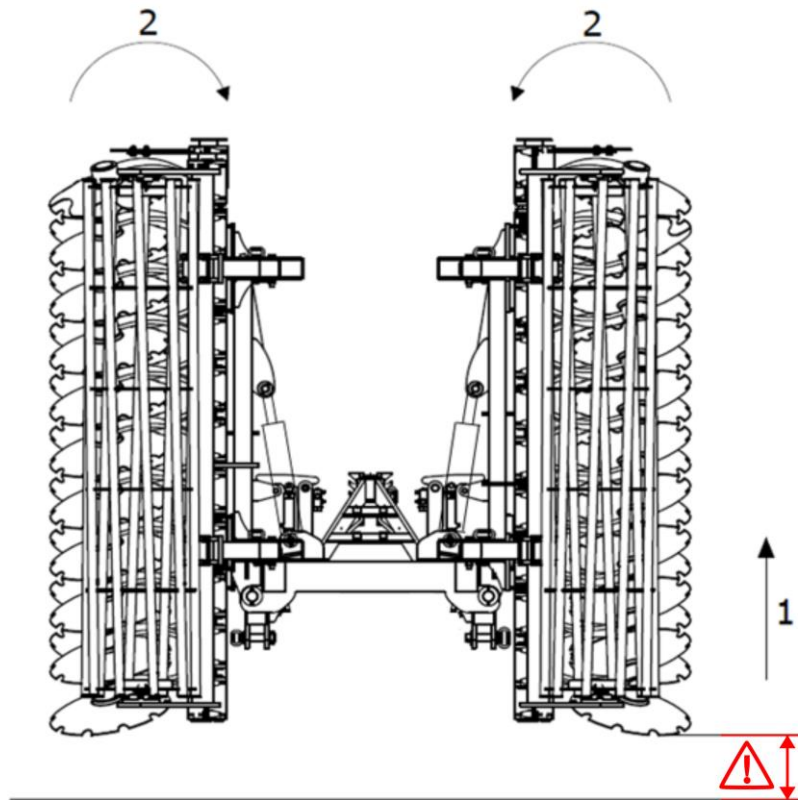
Séquence d'ouverture de la machine (1 - lever la machine au maximum (au moins 60 cm), 2 - déplier les ailes de la machine jusqu'à la position « fermée ».)
